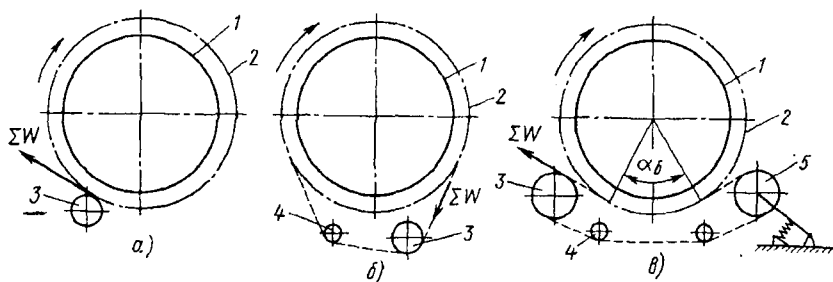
Приводы сушильных барабанов: а – шестерчатый; б – цепной охватывающего типа; в – цепной тангенциального типа; 1 – обечайка сушильного барабана; 2 – делительная окружность ведомого зубчатого венца; 3 – ведущее зубчатое колесо; 4 – обводные ролики; 5 – натяжное зубчатое колесо; ΣW – окружное усилие, ведущего звена, приложенное к зубчатому колесу.
